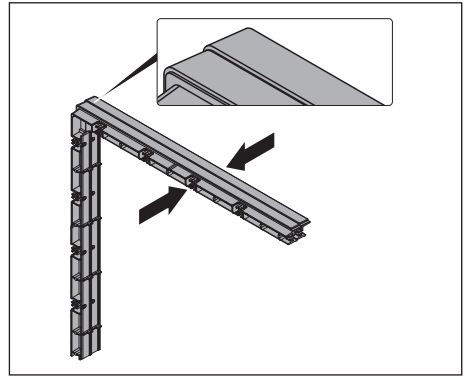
Demontaż ramowych elementów dystansowych
